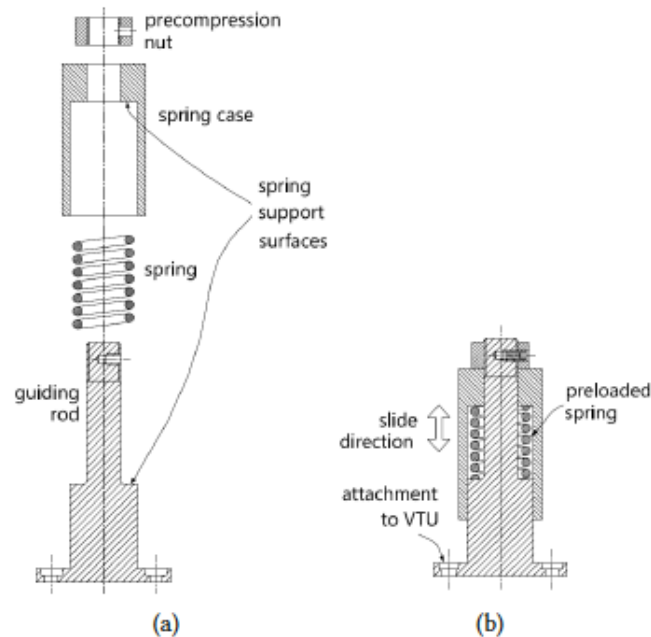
Representació esquemàtica de la unitat de regulació de la força. a) Vista explosionada. b) Parts acoblades i compressió de la molla. ^[21]
